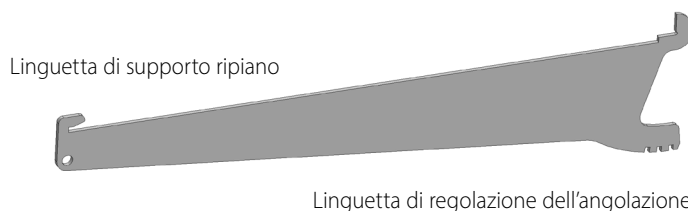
Identificazione linguetta staffa di supporto ripiano.
